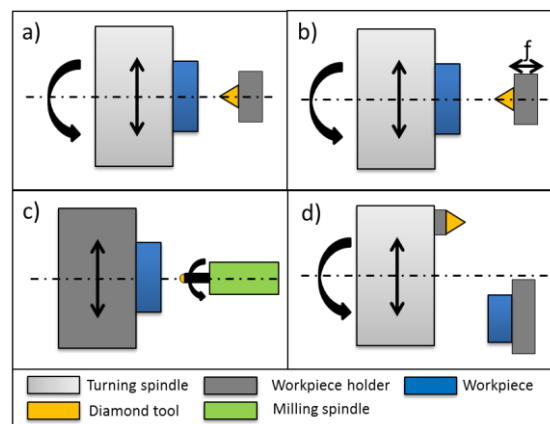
Prozessvarianten der Ultrapräzisionsbearbeitung a) UP-Drehen, b) Slow-Tool oder Fast-Tool Drehen, c) UP-Fräsen und d) Fly-Cutting [63]
